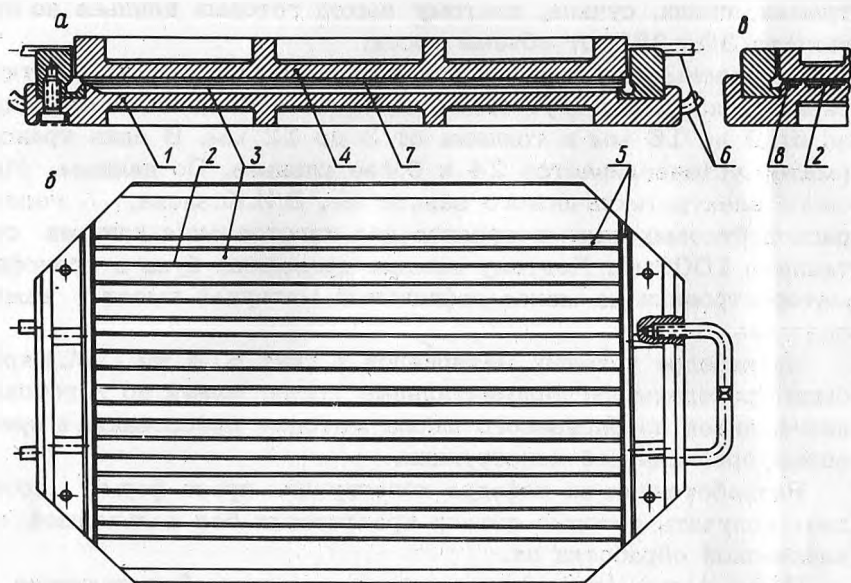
Пресс-форма с рассекателями для получения трансформаторных клиньев из шпона: а — продольный разрез пресс-формы в собранном виде; б) — матрица (вид сверху); в — поперечный разрез пресс-формы с запрессованными клиньями: 1 — матрица; 2 — рассекающие ножи; 3 — впадины; 4 — пуансон; 5 — отсекатели; 6 — ручки; 7 — пакет шпона; 8 — готовые изделия — клинья.
